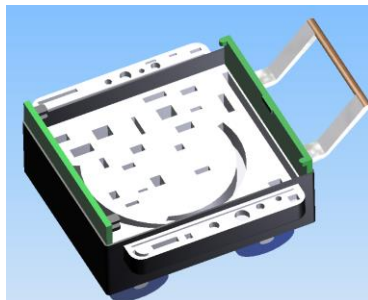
Výrobní layout varianta 2 pohled 3D
